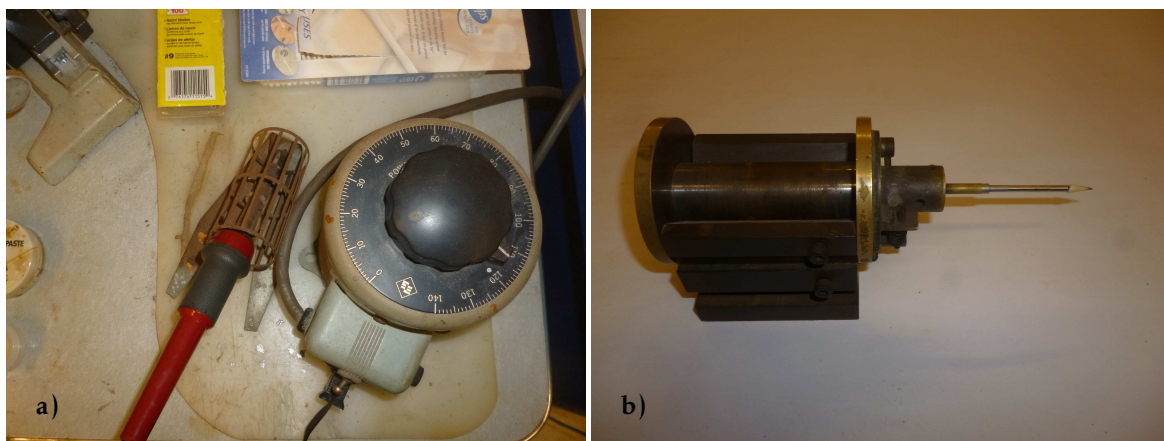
a) Soldador y b) portaprobetas.
